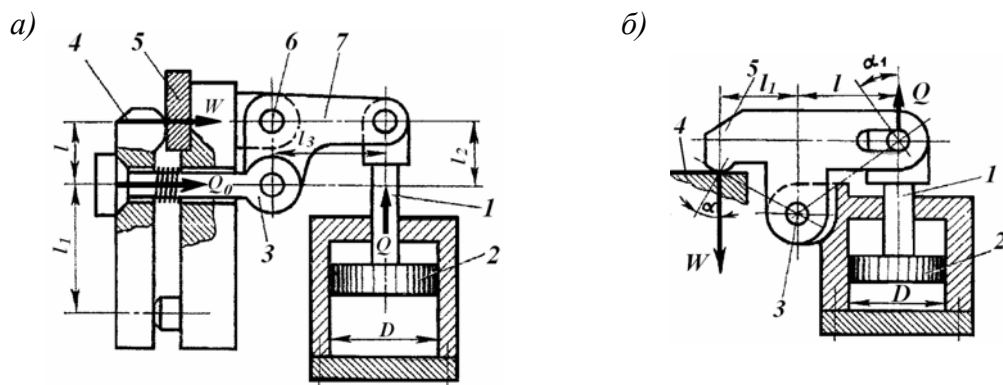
Конструктивные схемы рычажных шарнирных усилителей зажимных устройств с пневмоприводом
